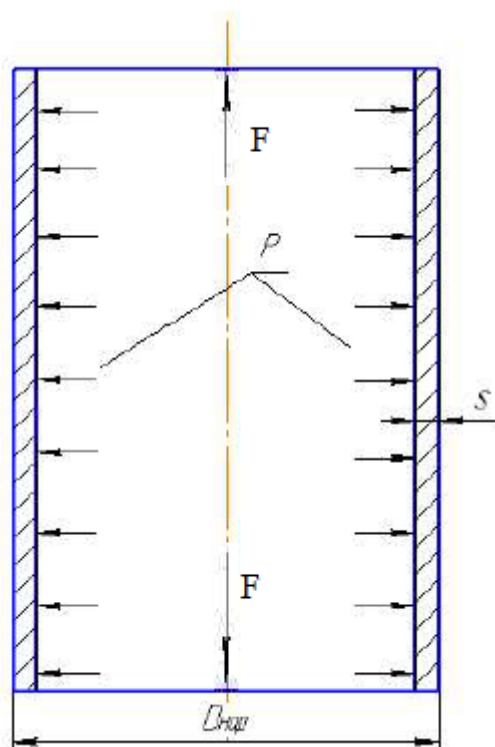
Расчетная схема цилиндрической обечайки камеры №2
